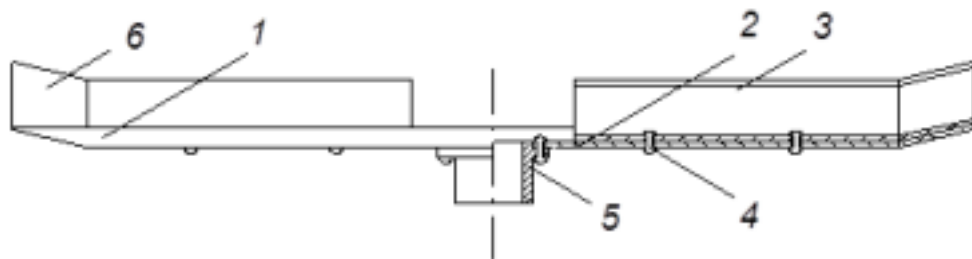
Схема відцентрового ТРО з плоским диском, який обладнаний конусною обичайкою: 1 - конусна обичайка; 2 - плоский диск; 3 – лопатка; 4 – заклепка; 5 - маточина; 6 - подовжувач лопатки
